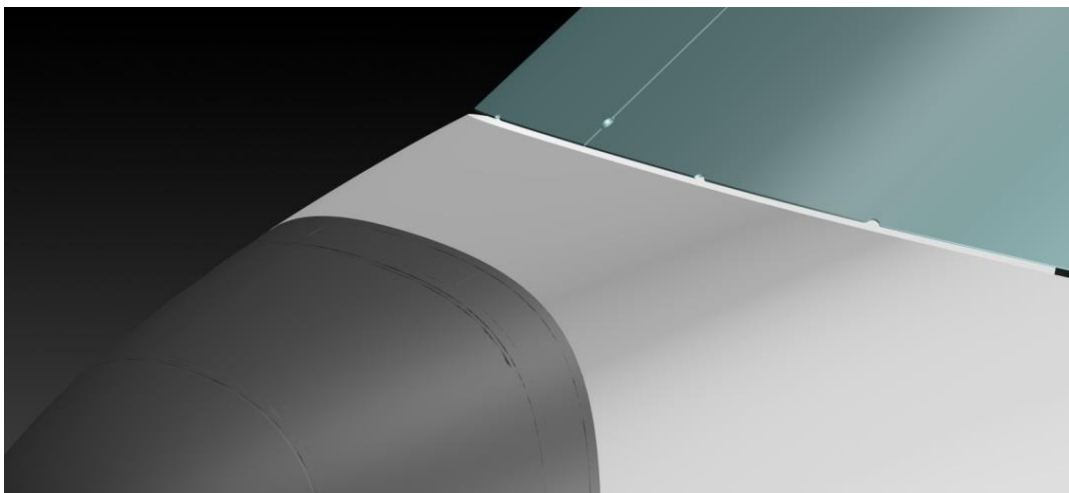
Вид стыковки кока носового со скрытым механизмом навески
